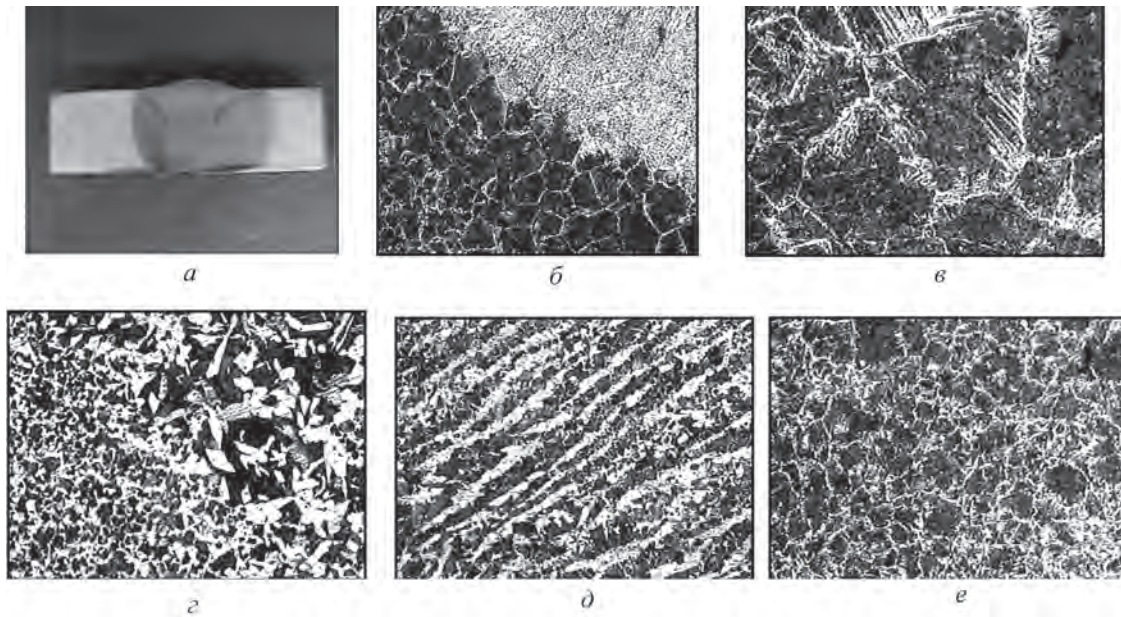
Макрошлиф (а) и микроструктура (б–е) сварного шва, полученного ручной электродуговой сваркой; б – зона сплавления; в – зона перегрева; г – зона нормализации; д – структура основного металла цапфы; е – структура основного металла кожуха картера
